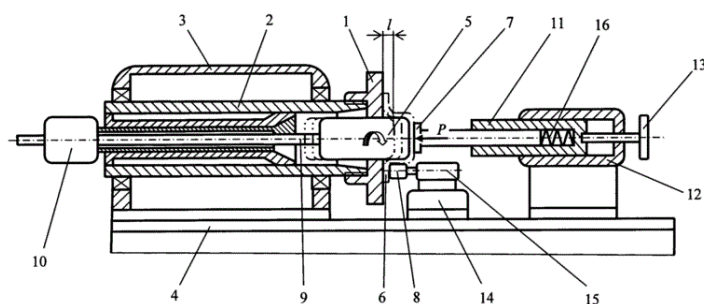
Конструктивная схема станка для формообразования полых деталей способом обкатки: 1- плоская матрица; 2-шпindelь передней бабки; 3- передняя бабка; 4- станина станка; 5- профильная оправка; 6- тонколистовая заготовка; 7- прижимная пята; 8- обкатной ролик; 9- хвостовик оправки; 10 – механизм ступенчатой подачи и фиксирования оправки; 11- пиноль задней бабки; 12- задняя бабка; 13 – привод прижима; 14- суппорт; 15- виброустройство; 16- прижим
